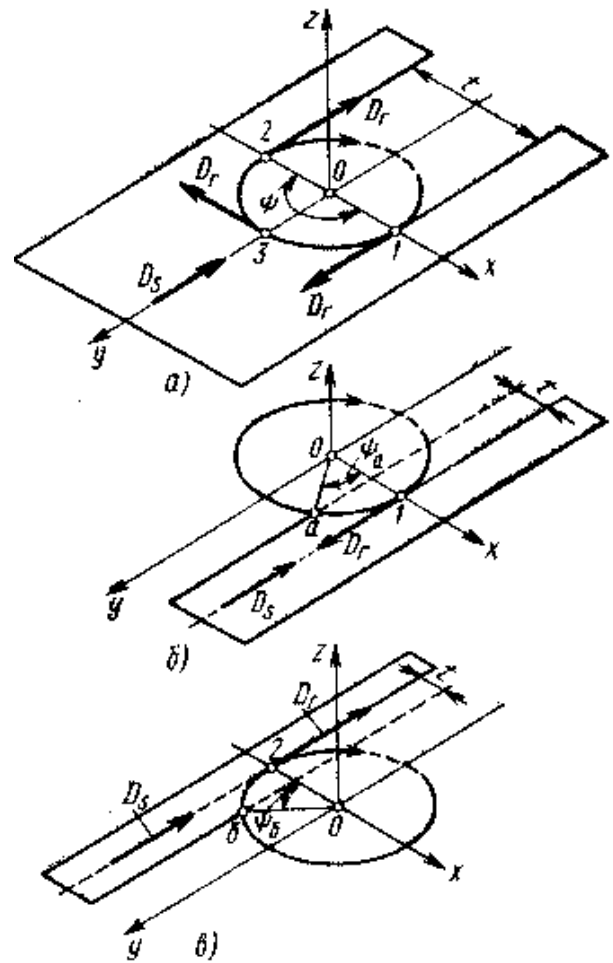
Схеми торцевого фрезерування при різних кутах контакту: а) лобове; б) в умовах зустрічного фрезерування; в) в умовах попутного фрезерування.
